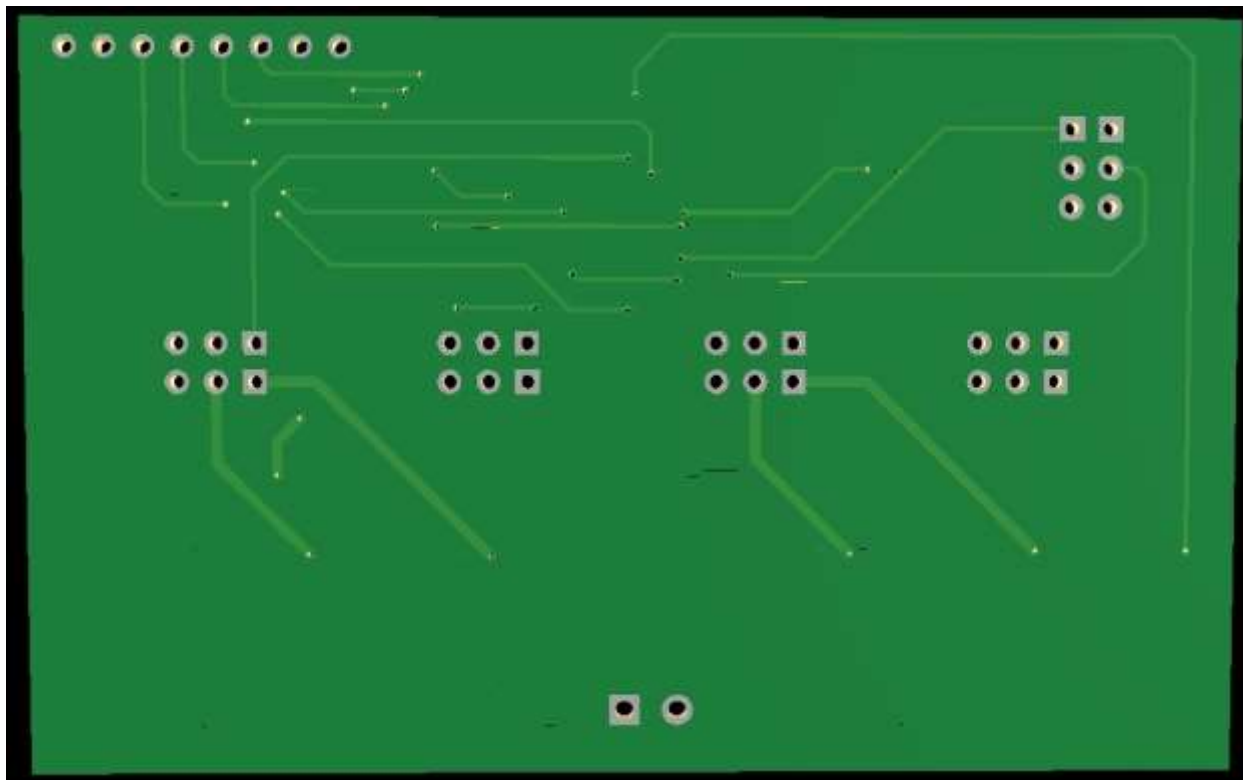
Τελικό σχέδιο του PCB [10]
